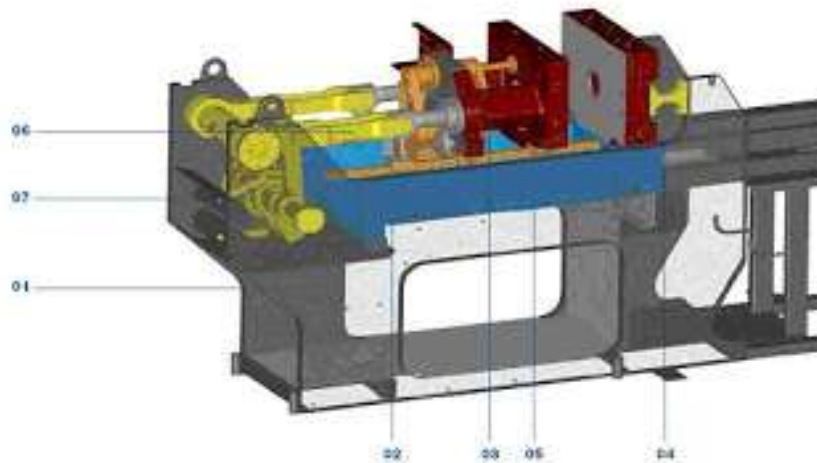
Cierre tipo rodillera convencional. [5]
